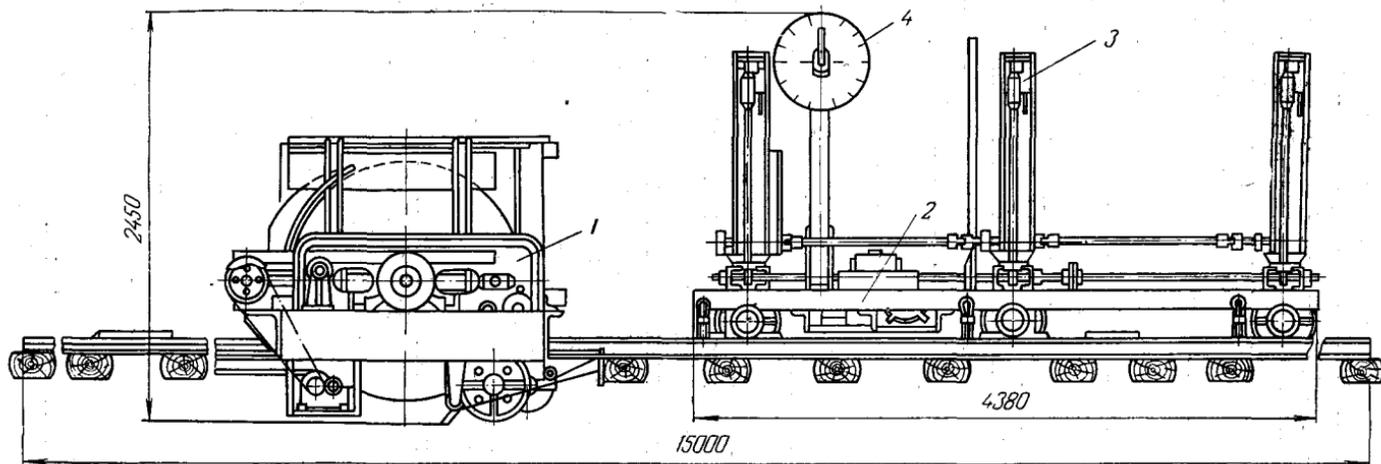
Однопильный круглопильный станок для распиловки бревен:
